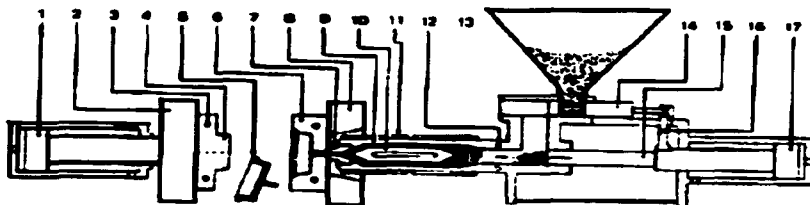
Diagrama simplificado de una máquina de moldeo por inyección todo pistón. Todos los componentes móviles de la máquina están representados al finalizar el ciclo. Nótese que la pieza moldeada (5) es expulsada del molde. 1. Pistón del cierre del molde 2. Platina móvil 3. Circuito de agua para el enfriamiento del molde 4. Medio molde móvil 5. Pieza moldeada 6. Medio molde fijo 7. Boquilla 8. Platina fija 9. Cilindro de plastificación 10. Torpedo 11. Resistencia eléctrica para calentamiento de cilindro de inyección 12. Tolva 13. Pistón de inyección 14. Brazo que actúa el dosificador 15. Pistón hidráulico
